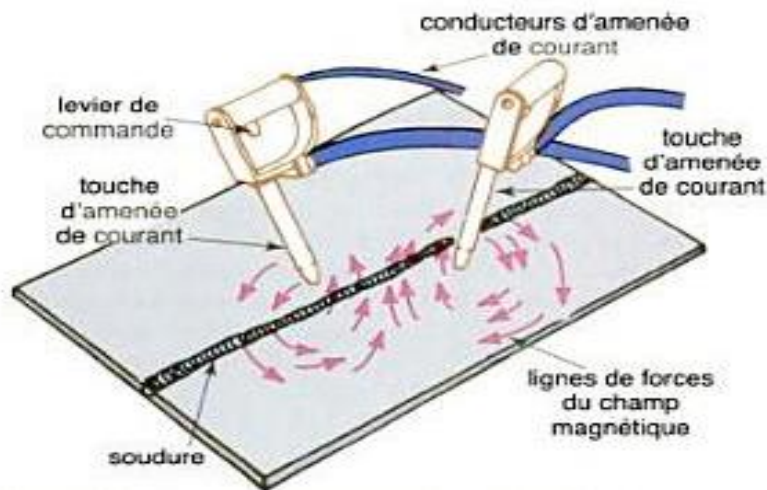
Un champ magnétique est créé près d'une soudure par le passage, au travers de la soudure, d'un courant électrique allant d'une touche à l'autre. [22]
